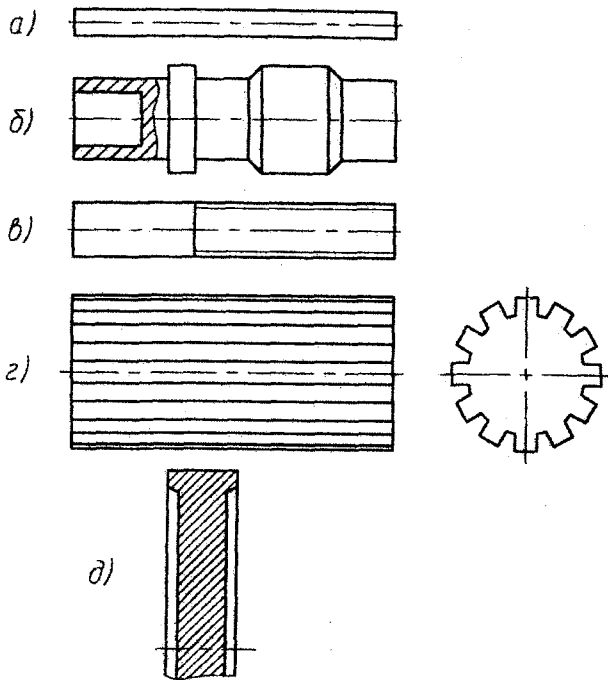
Детали, изготавливаемые штамповкой с обкатыванием: а) калиброванные оси; б) ступенчатые валы, в том числе полые; в) валы с резьбой; г) валы со шлицами; д) плоские детали с бортом
